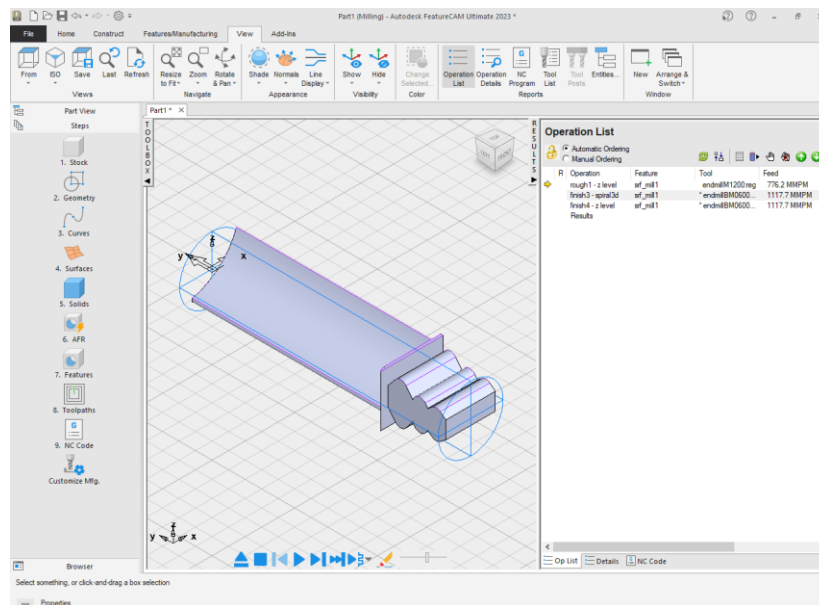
Вибір форми заготовки для лопатки газотурбінного двигуна
